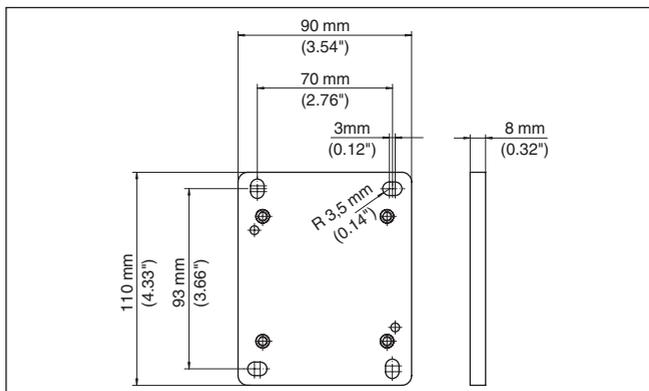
Gabarito dos orifícios - Placa de montagem na parede
